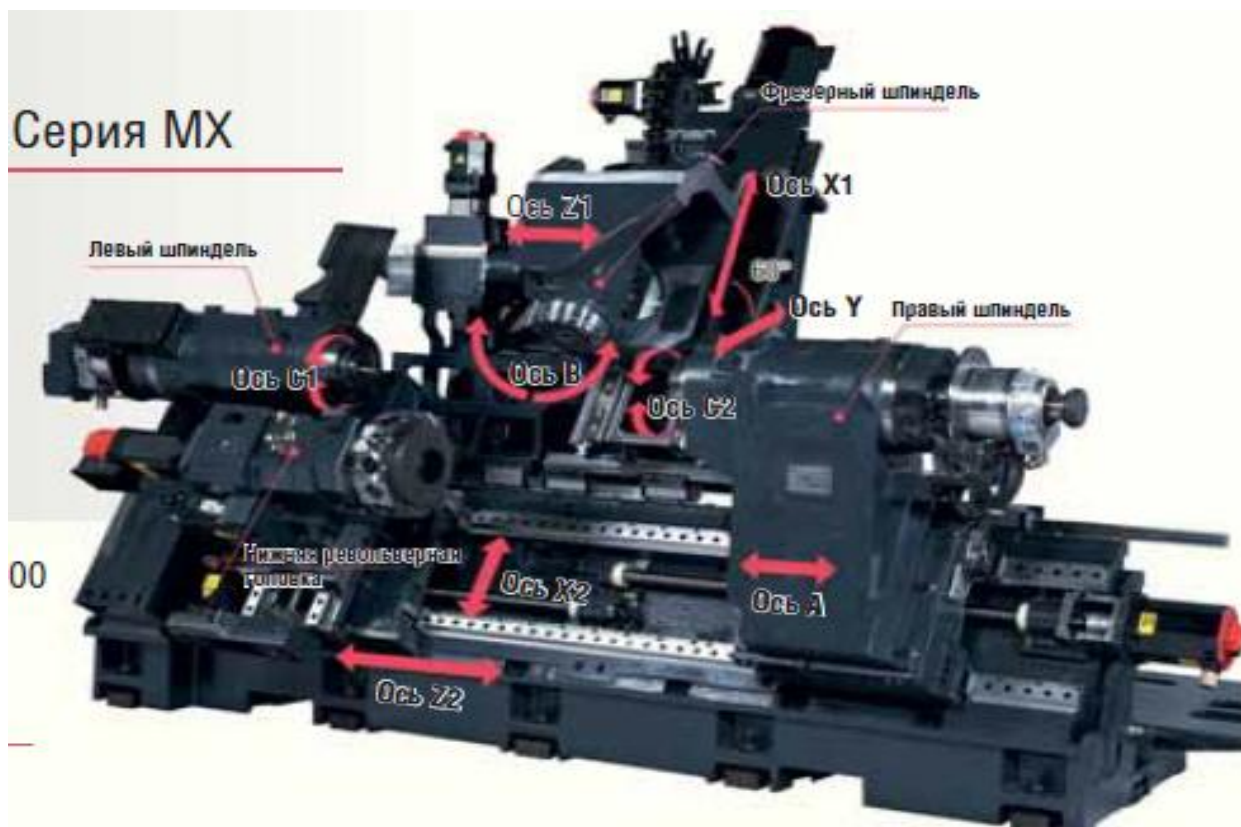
Компоновка обрабатывающего центра с ЧПУ PUMA MX2100ST
